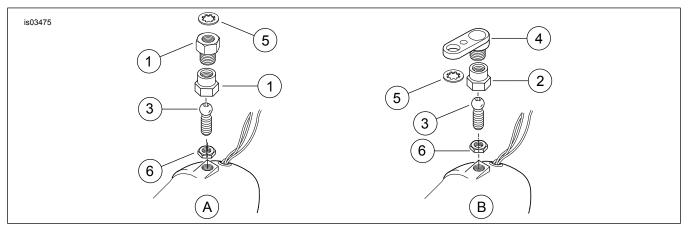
Instalación de los pivotes delanteros y las señales de giro
